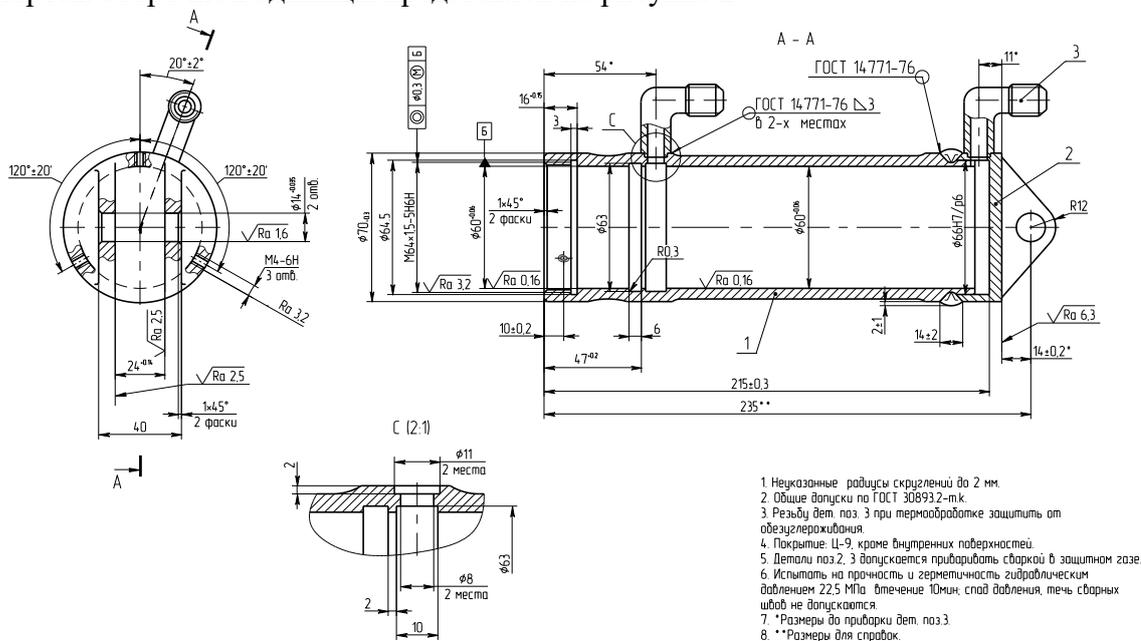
Сборочный чертеж цилиндра гидроусилителя руля
